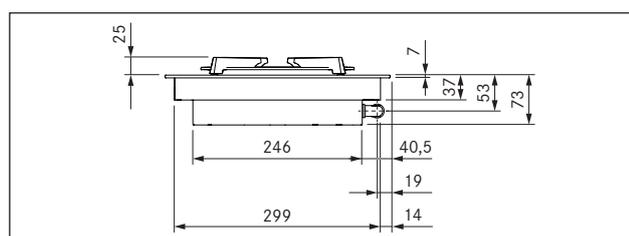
Dimensioni apparecchio CKG vista frontale
